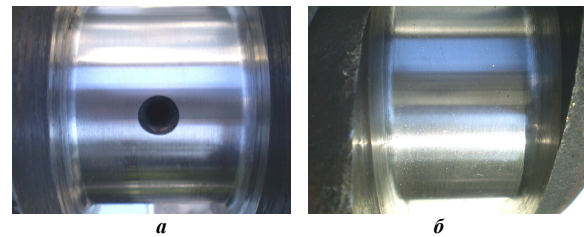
Загальний вид робочої поверхні корінної та шатунної шийки сталевого колінчастого валу двигуна 4ЧН 12/14 до зміцнення:
